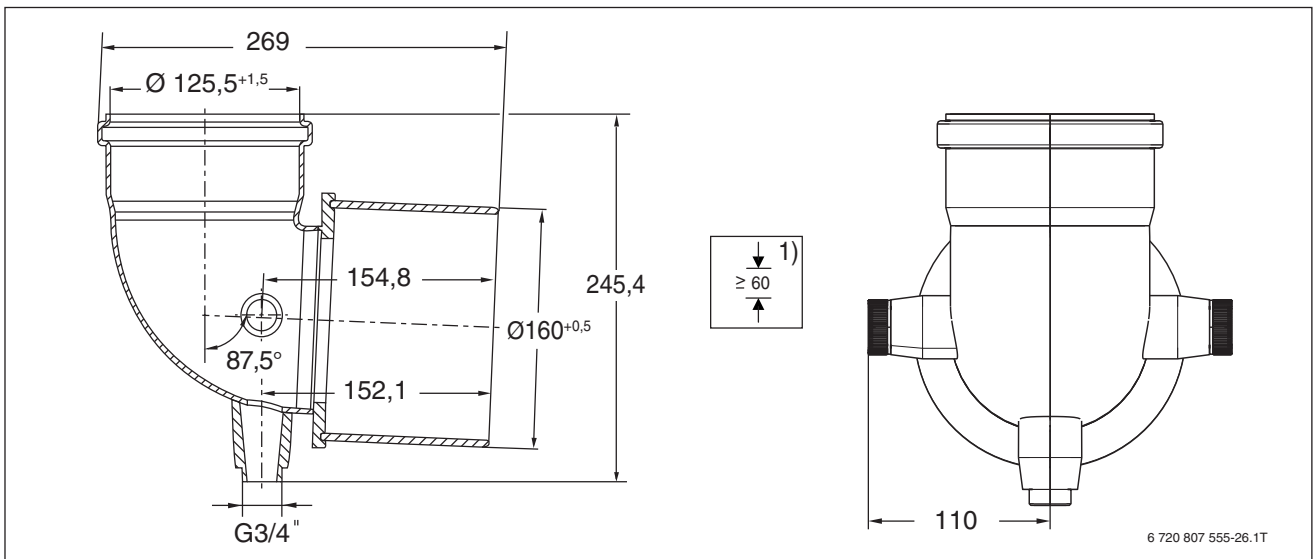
Anschlusswinkel 87° DN 160/125 (Maße in mm)
